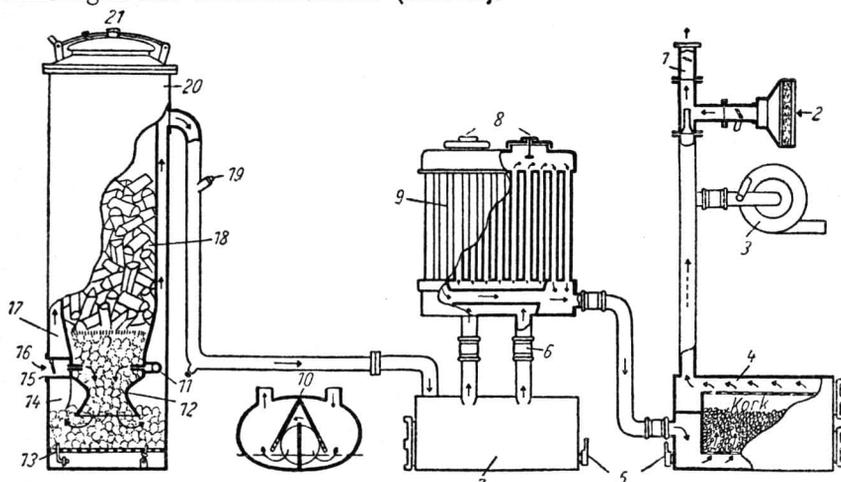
Der Holzgaszerzeuger mit Kühler und Reiniger (Schema)
